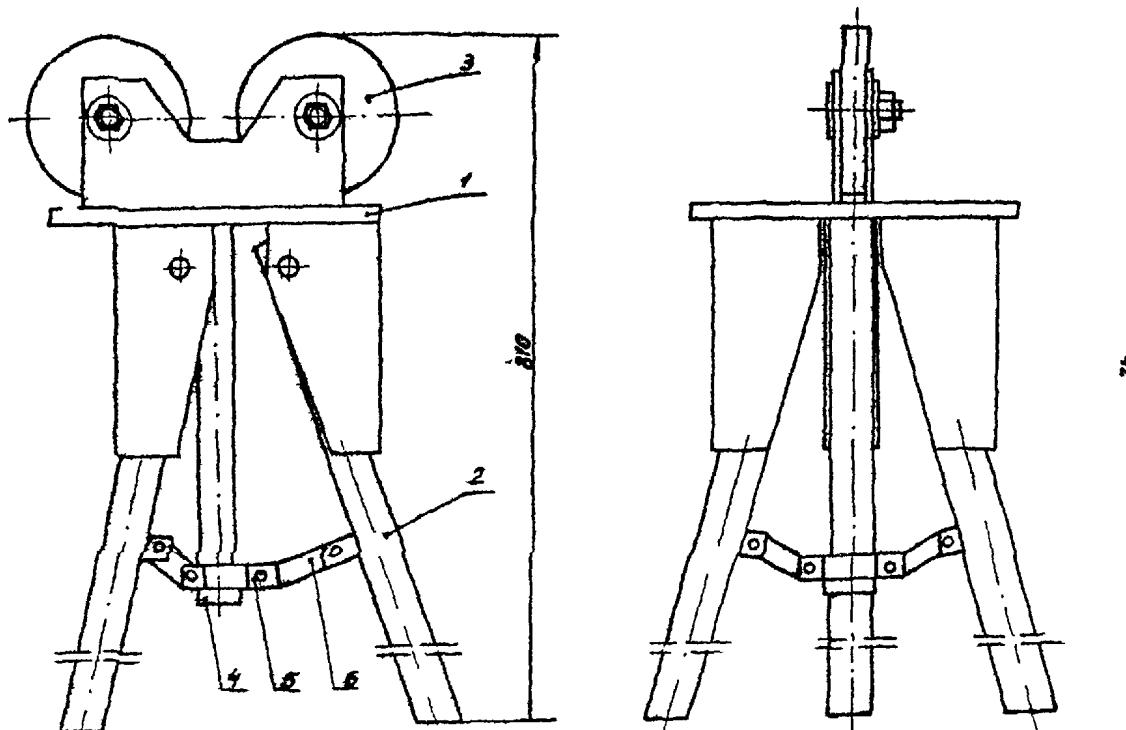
Рис. I. Подставка для укладки деталей тормозной системы: 1 - основание ; 2 - ножка ;
